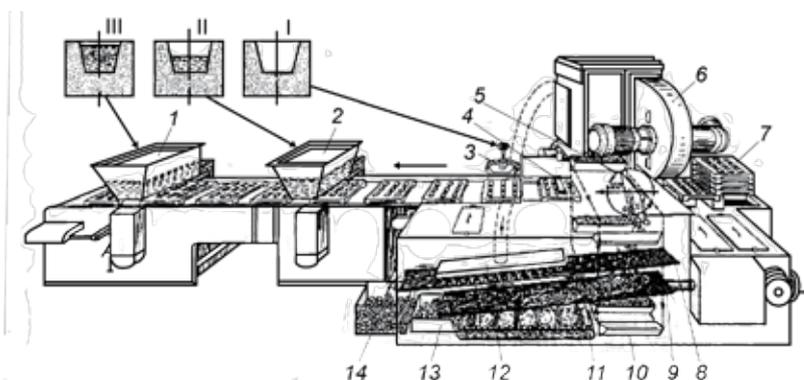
Схема конфетоотливочной машины с двумя отливочными механизмами
